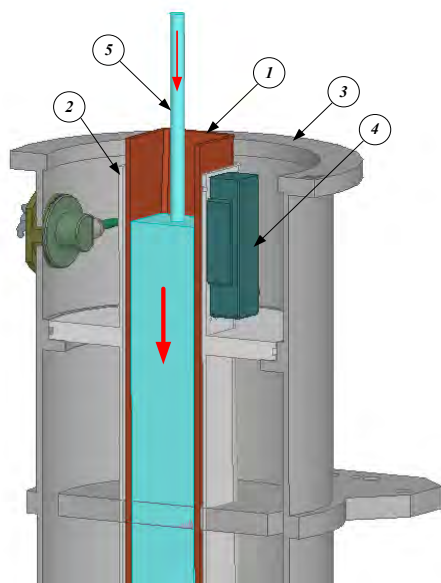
Основные узлы сортового кристаллизатора: 1 – гильза, 2 – нержавеющая обечайка, 3 – корпус, 4 – датчик уровня металла, 5 – жидкий металл
